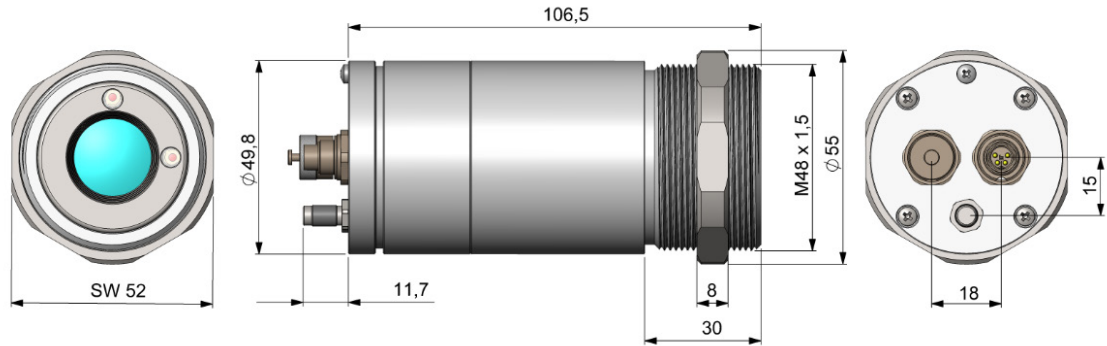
Maßzeichnung thermoMETER CSVideo Sensor
